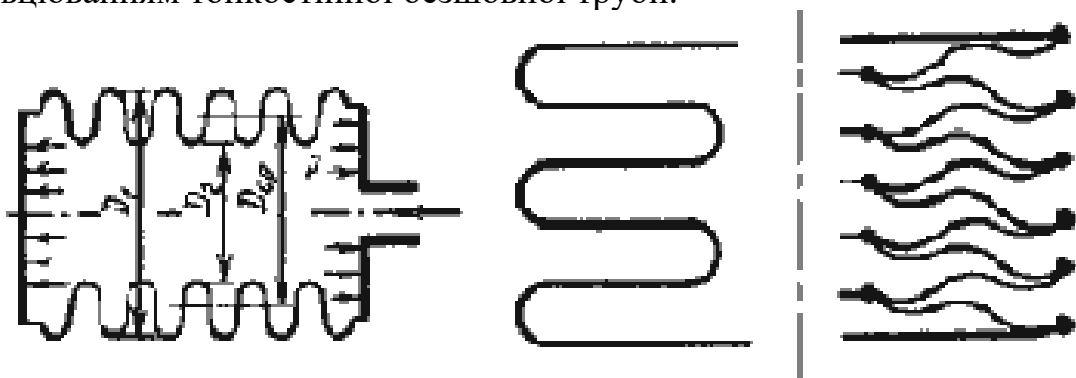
Схема металевого сильфона: а - сильфон; б - цільна стінка; в - зварна стінка
